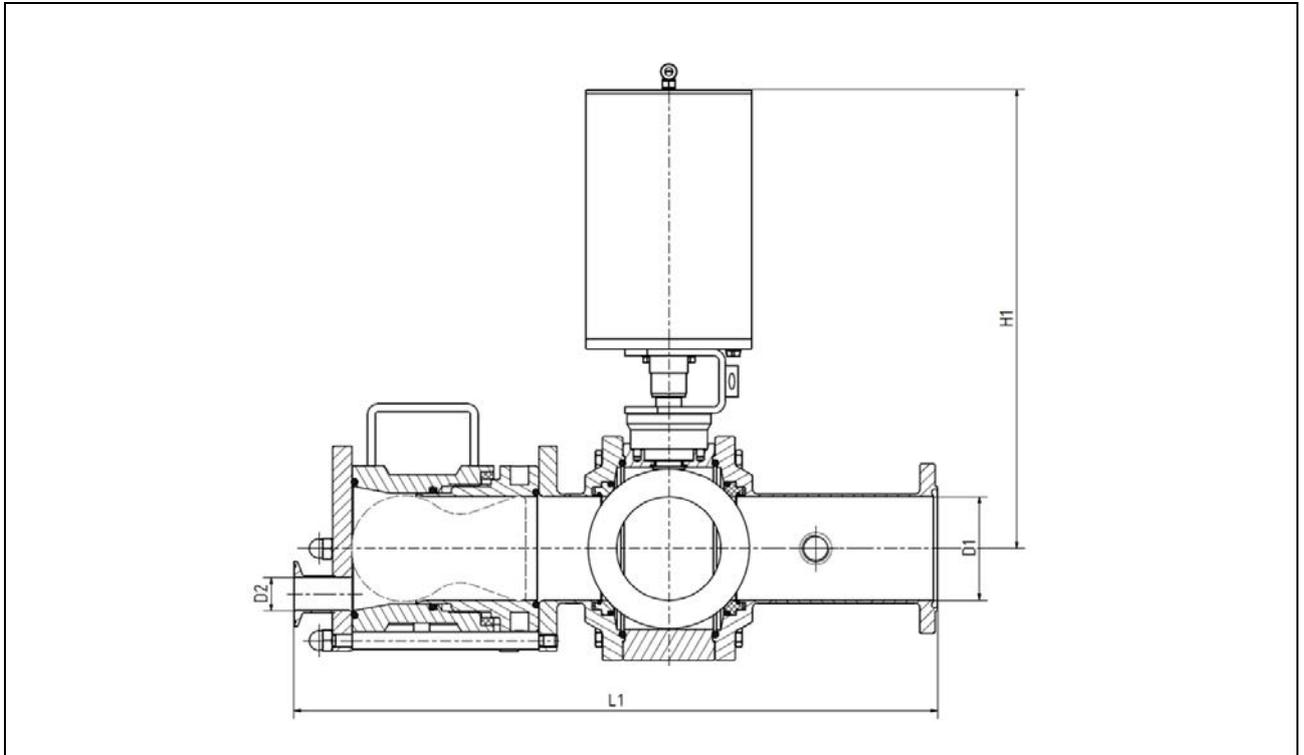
Steckkammer mit Kugelventil, Anschlussvariante DIN, Serie A
